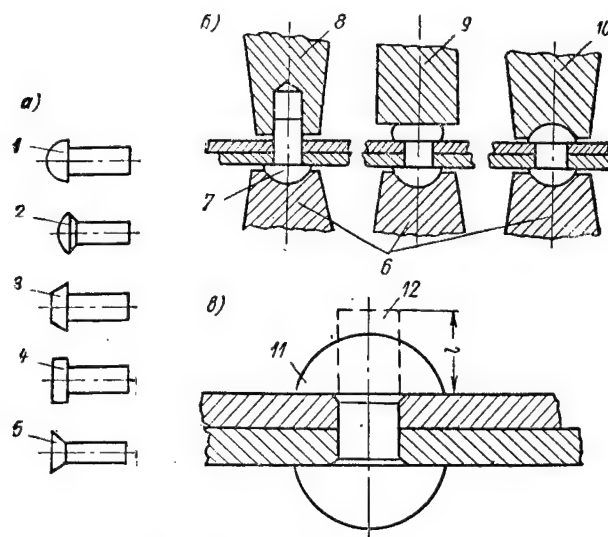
Клепка и виды заклепок: а — виды заклепок; б — схема клепки; в — схема образования полукруглой замыкающей головки.
